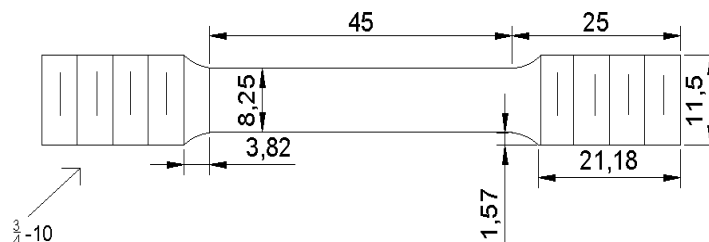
Dimensões do corpo de prova para ensaio de fadiga flexo-rotativa.
